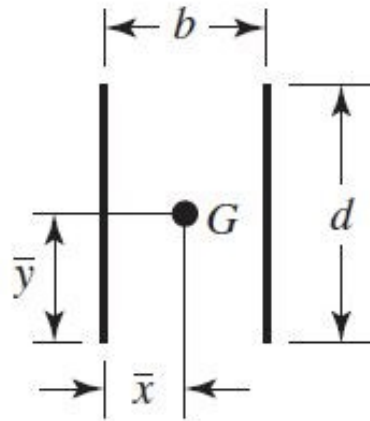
Patrón de soldadura cordones verticales, [31].
